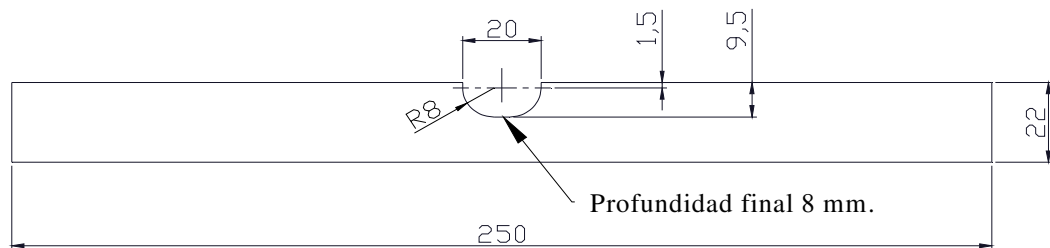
Ranura en cupón de soldadura de 250x130x22 mm.
